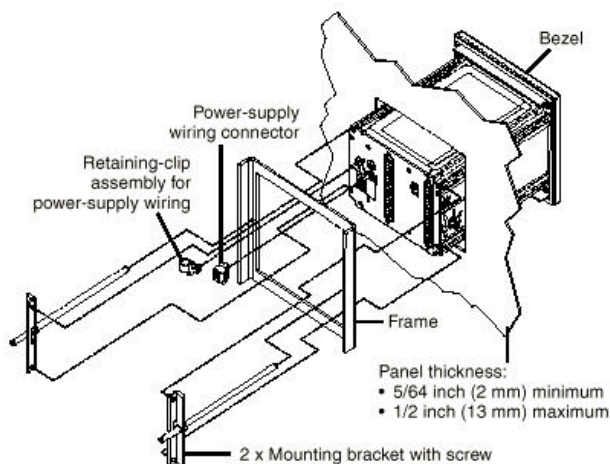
Montaje del controlador de Batch Discreto 3300.
